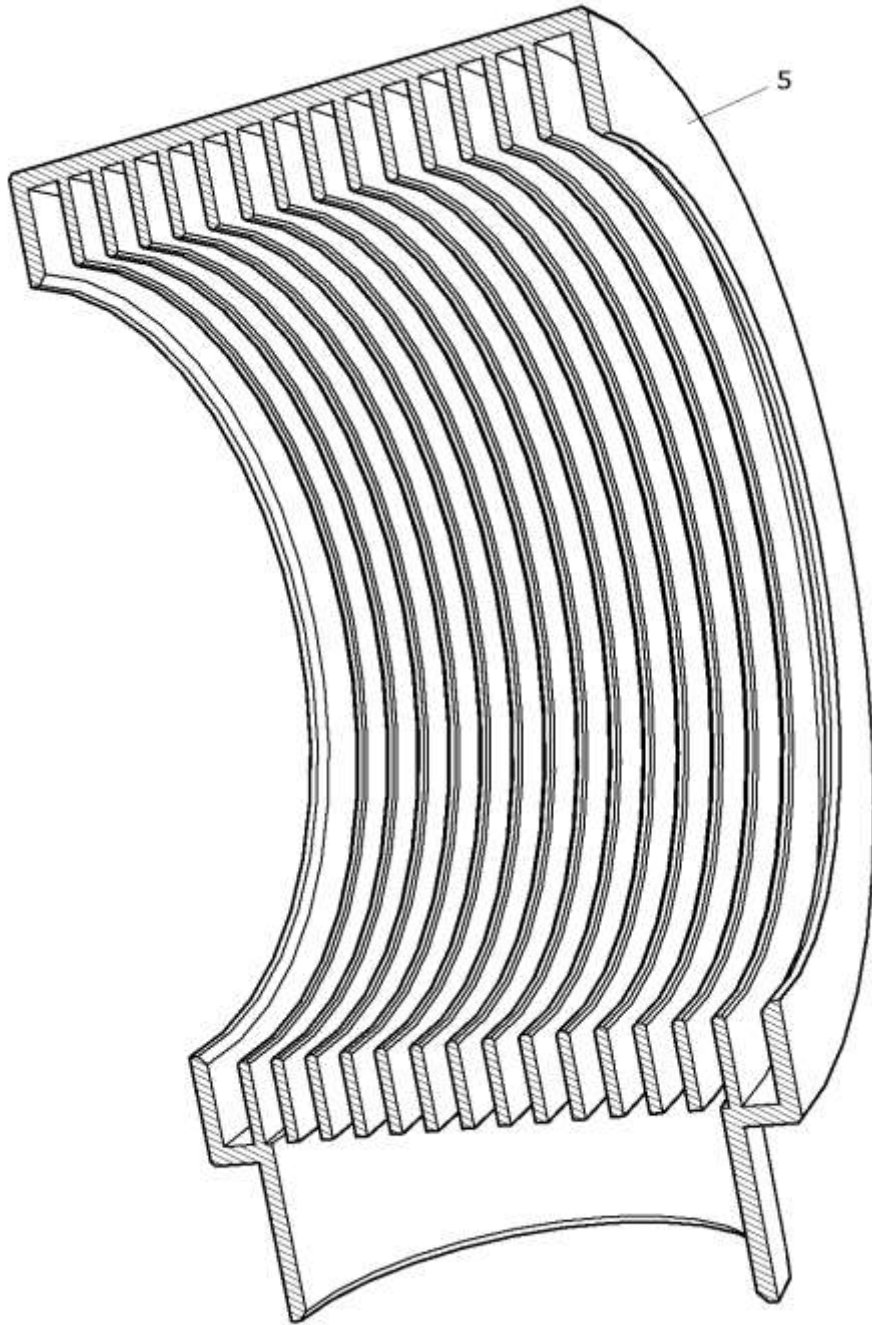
Drehkolben-Stirlingmotor, abgebaut bis vor die erste Ofendichtung.
